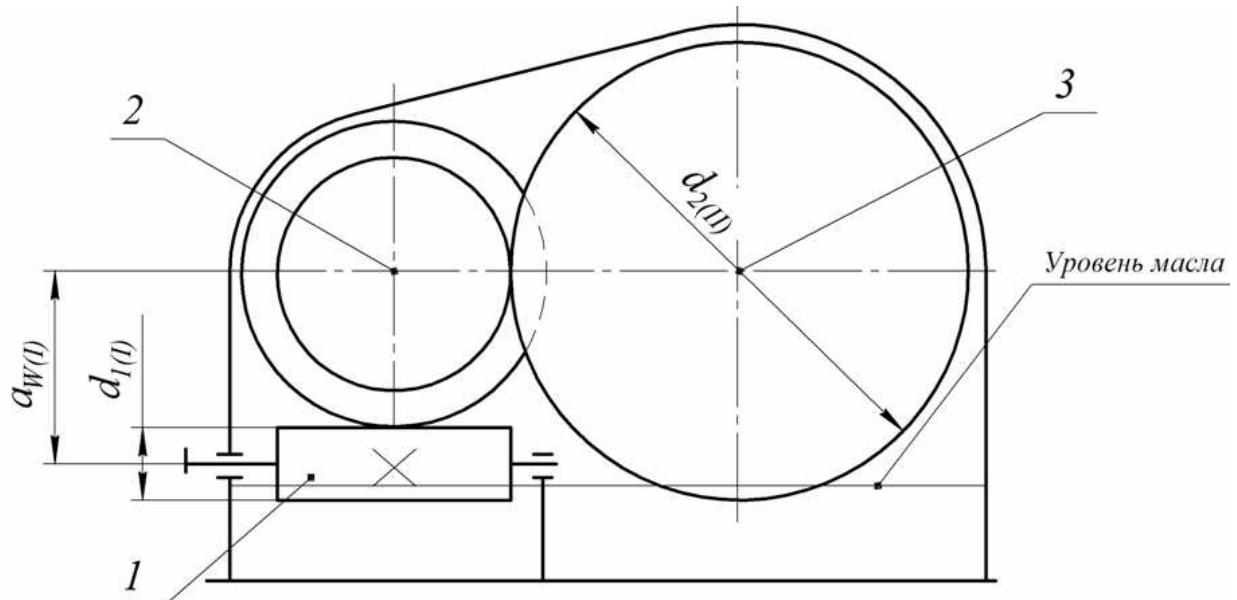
Редуктор ЧЦ с нижним расположением червяка
